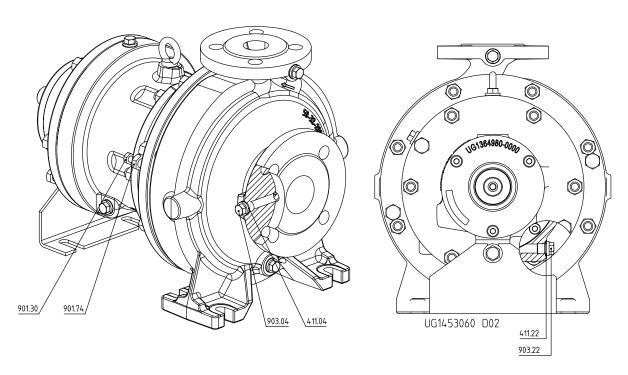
Befestigung Druckdeckel am Pumpengehäuse bei Ausführung mit geschraubtem Deckel
